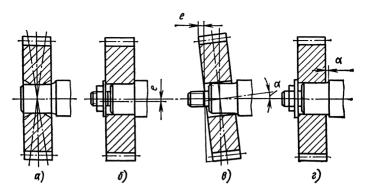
Погрешности установки зубчатых колес на валу: a — качение зубчатого колеса на шейке вала; δ — радиальное биение на шейке вала; ϵ — торцовое биение; ϵ — неплотное прилегание к упорному торцу
